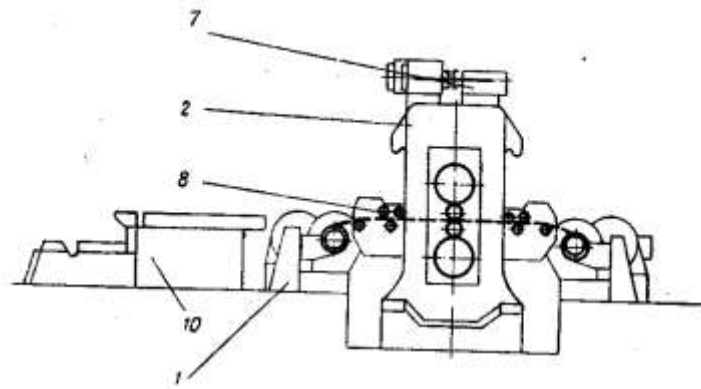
Кинематическая схема четырехвалкового реверсивного фольгопрокатного стана 160/450x750
